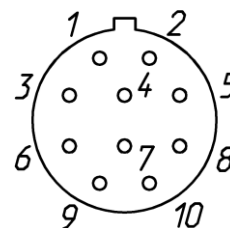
Розетка ОНЦ-БС-1-10/14-Р12-1-В вид со стороны контактов
